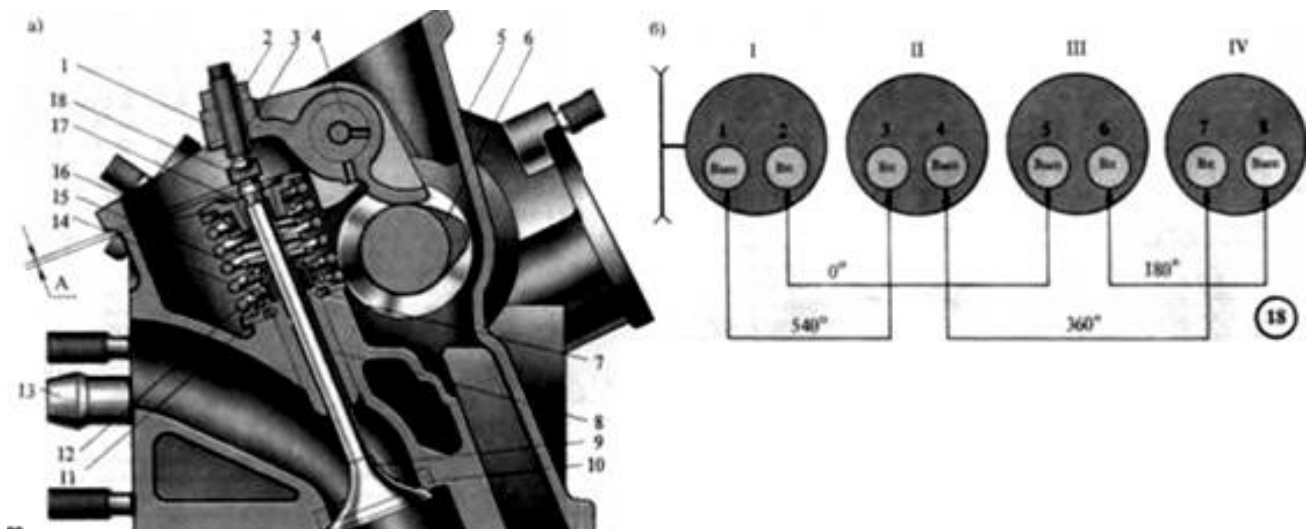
Головка (а) циліндрів (поперечний розріз) і схема (б) регулювання зазорів в механізмі приводу клапанів:
